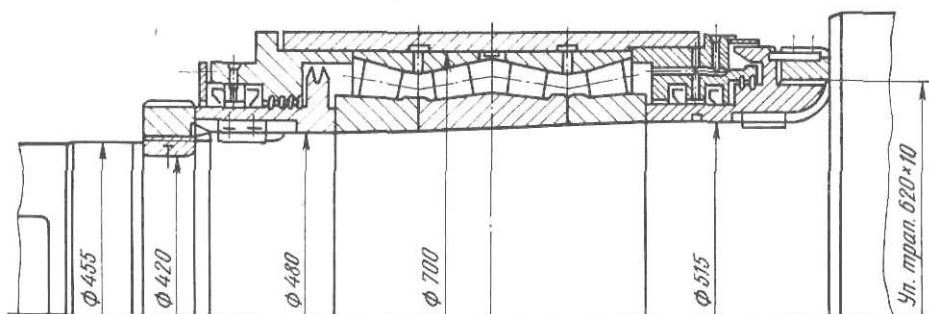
Установка рабочего валка с конической шейкой четырехвалкового стана 2000 на роликовых конических подшипниках
